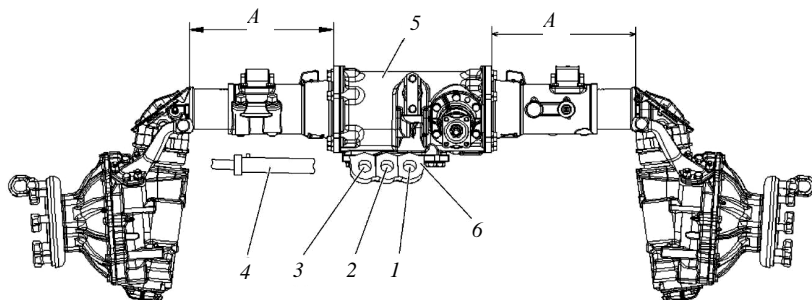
Схема переднего моста трактора с коническими колесными редукторами: 1, 2, 3 – отверстия для крепления цилиндра; 4 – цилиндр; 5 – ПВМ; 6 – кронштейн
